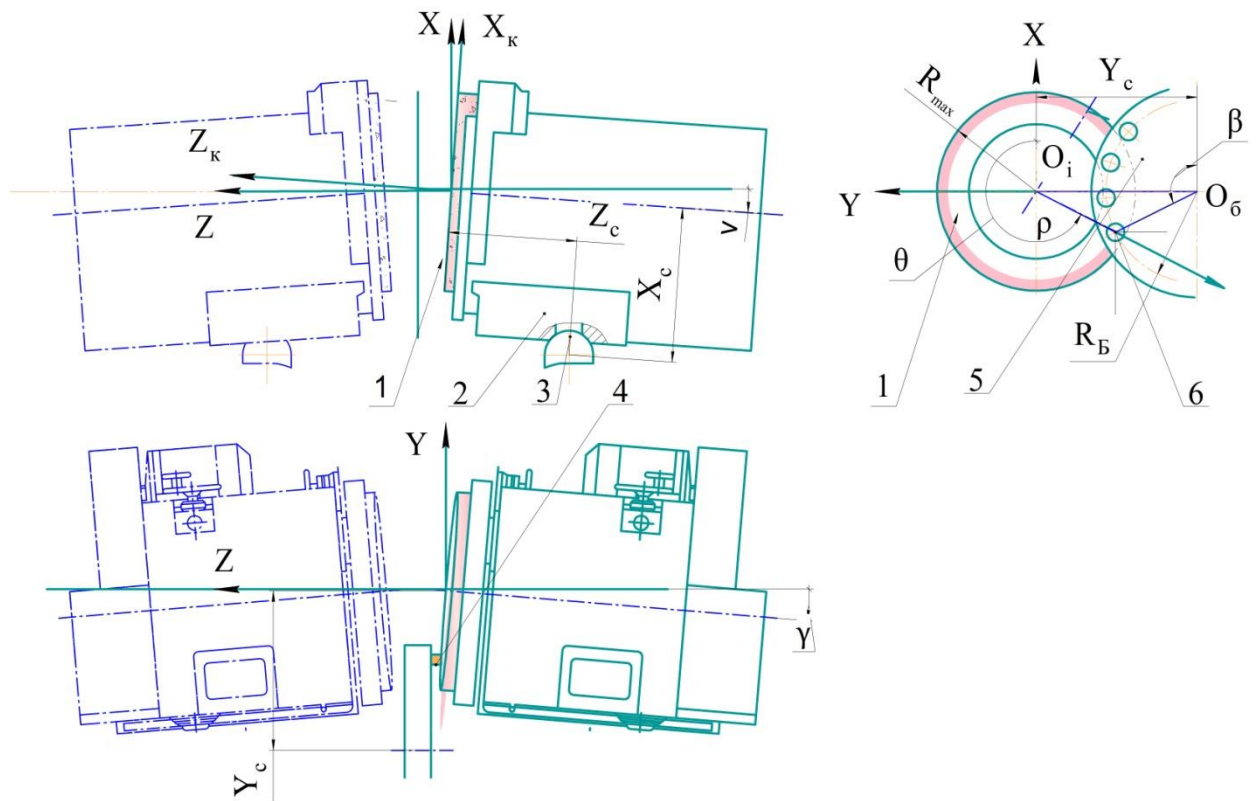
Схема наладки верстату 3342АДО на обробку торців деталей: 1 – шліфувальний круг з формотворною ділянкою; 2 – шліфувальна бабка; 3 – сферична опора; 4 – алмазний олівець; 5 – барабан подачі деталей з місцем встановлення алмазного олівця; 6 – деталь
